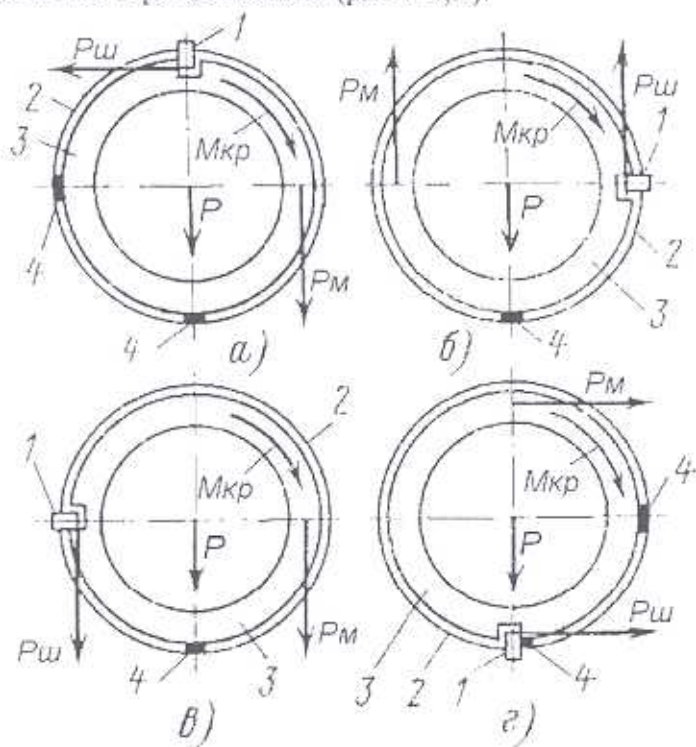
Схема центровки вкладыша на сухарях (колодках) [5]
